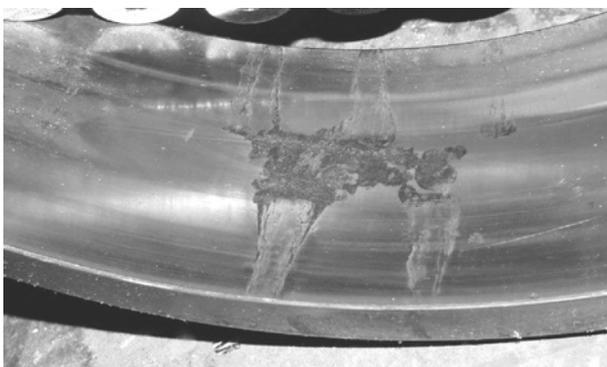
Следы местной коррозии наружного кольца подшипника
